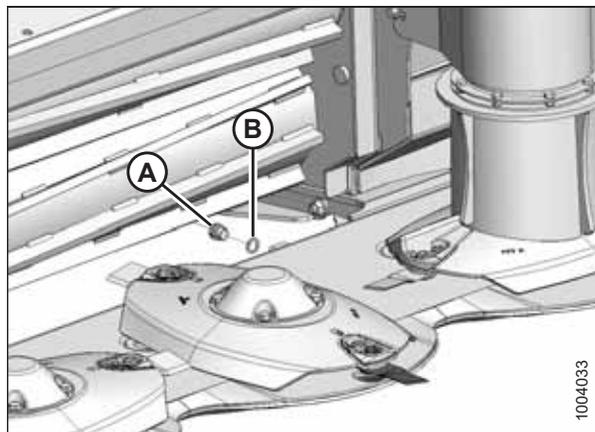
Bouchon d'inspection d'huile de barre de coupe
